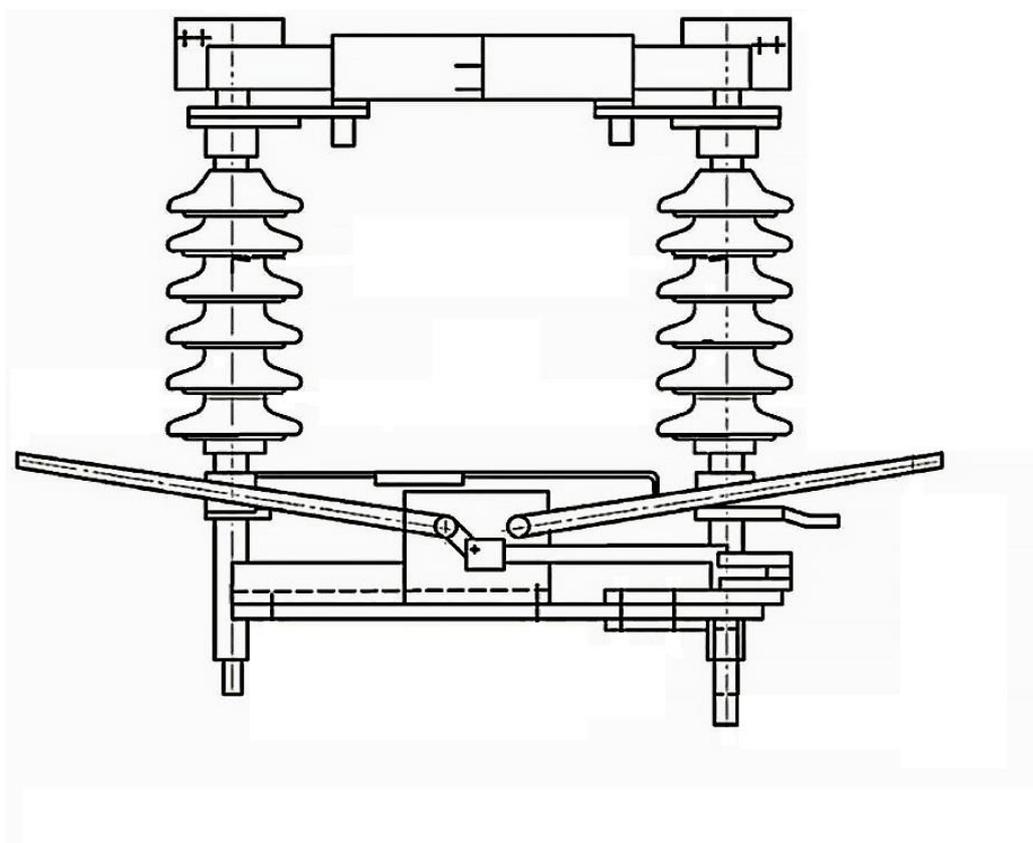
Внешний вид разъединителя марки РНДЗ-26-35/1000
